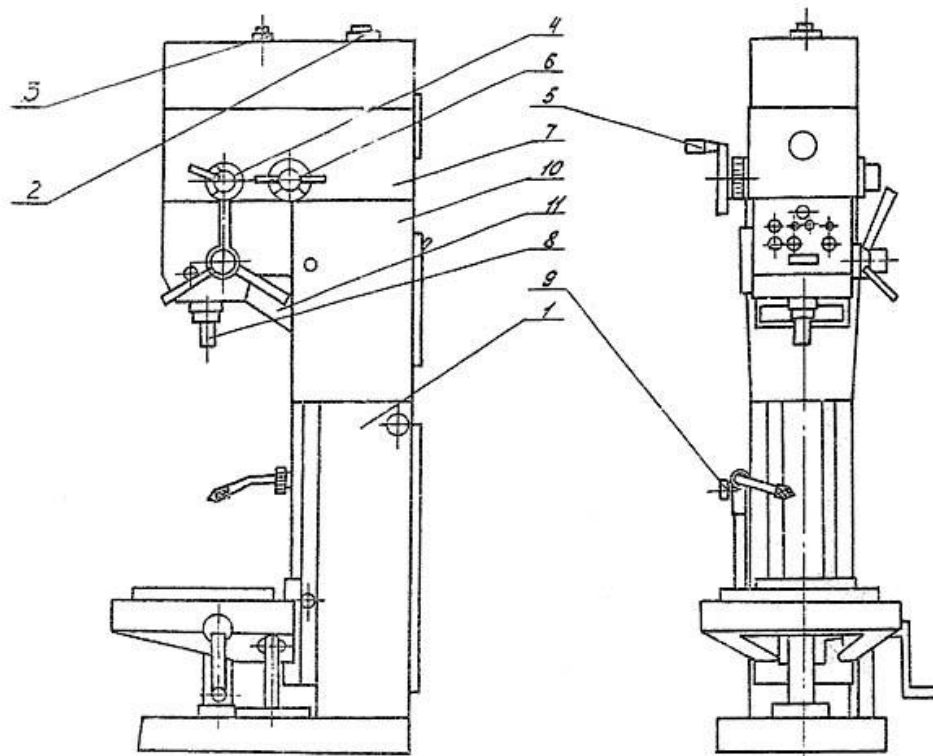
Основні частини вертикально-свердильного верстату
